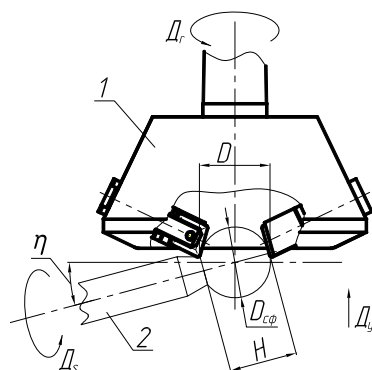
Схема комбинированной скоростной обработки сферической поверхности детали
